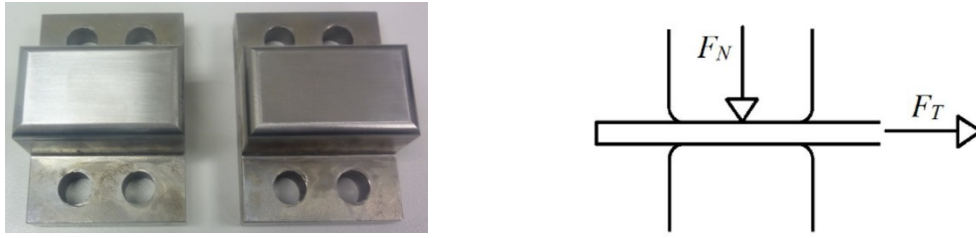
Representación esquemática de un ensayo Strip Drawing test.
